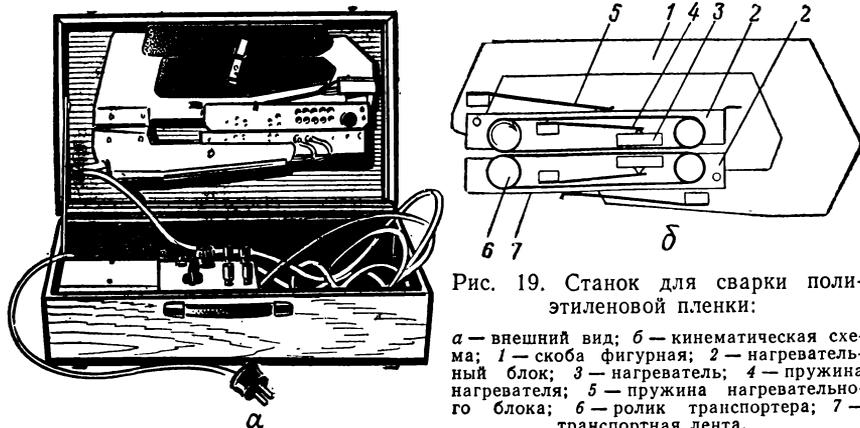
Станок для сварки полиэтиленовой пленки:
